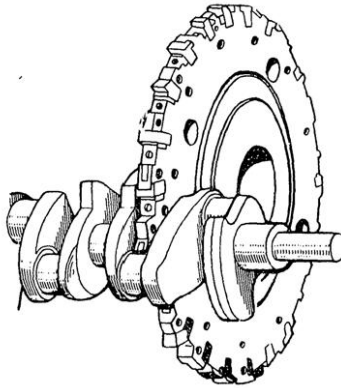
Ротационное фрезерование шатунной шейки заготовки коленчатого вала
